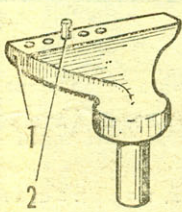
Давилник для работ на деревообрабатывающем токарном станке.
